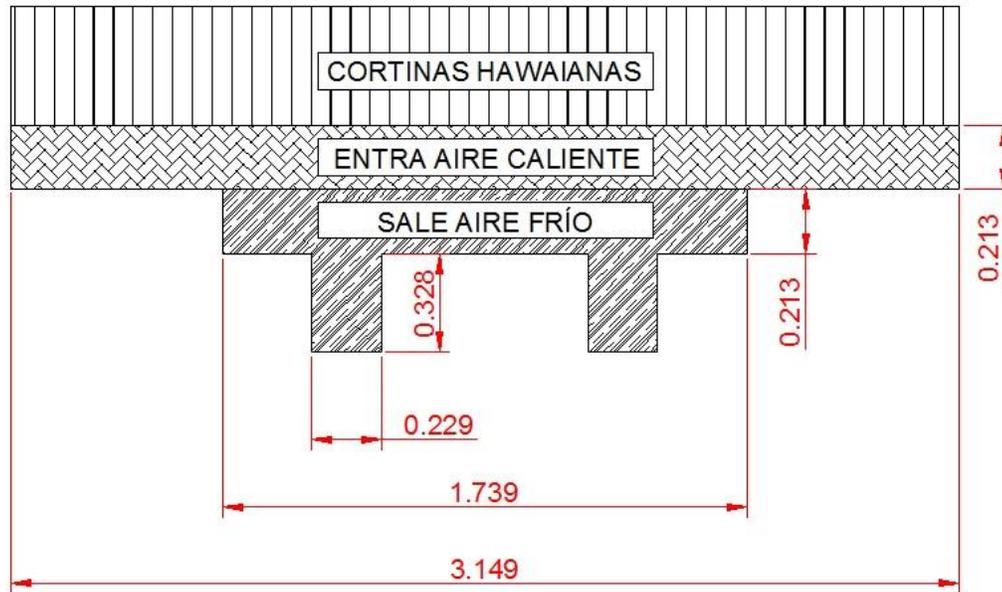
Plano de la abertura permanente de entrada y salida del IQF
